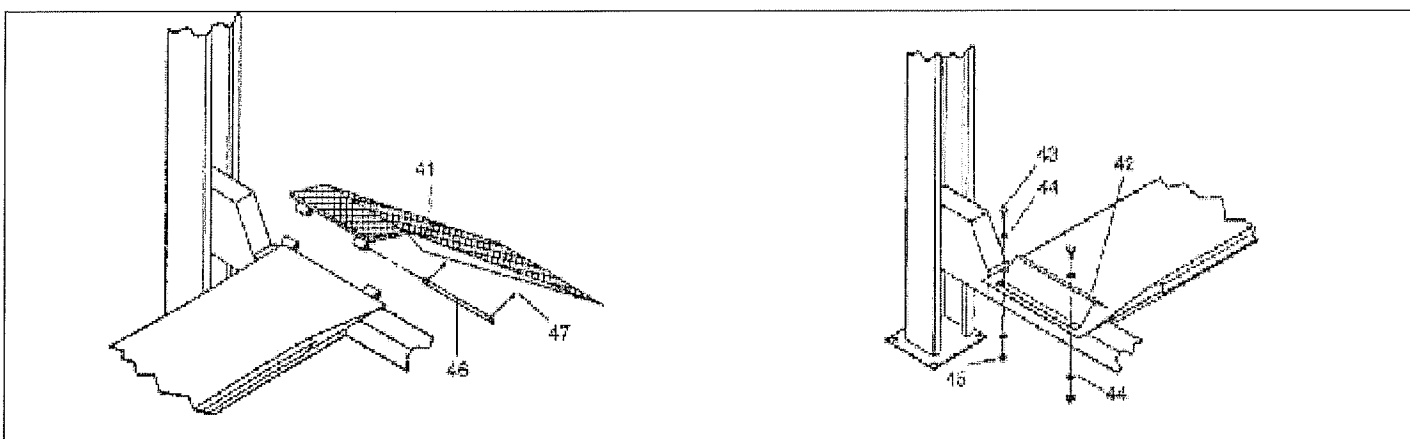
Крепление упоров колес и рампы заезда автомобиля
